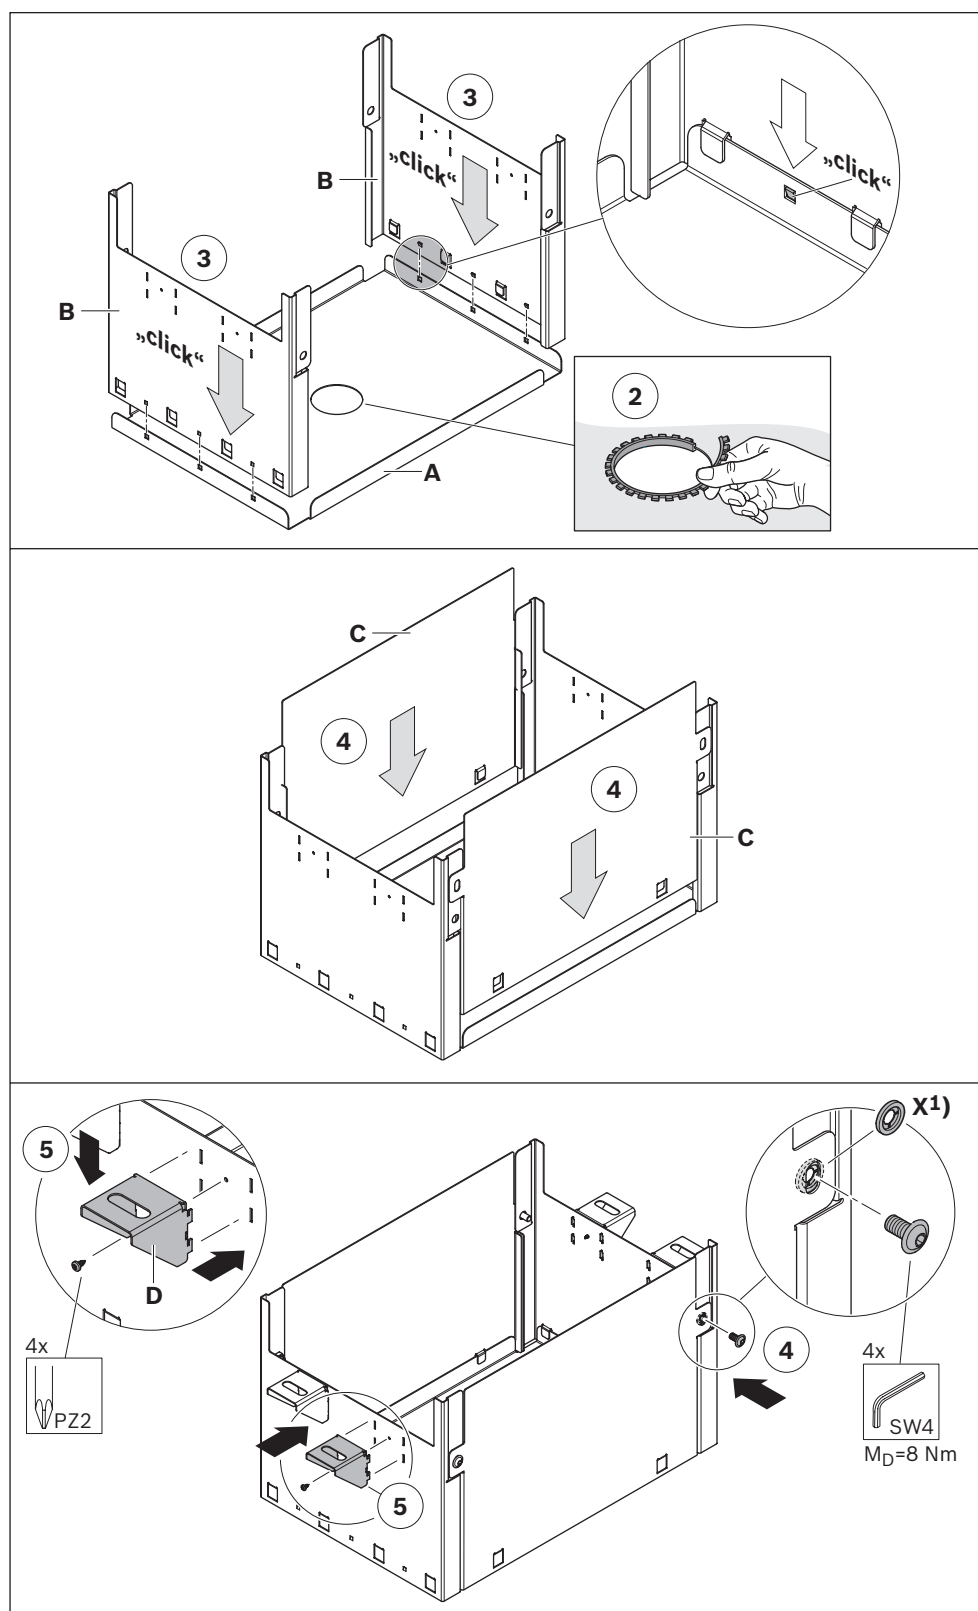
Premontaje de la caja de protección (aquí tamaño constructivo 2 180° para WT 2, WT 2/F)
